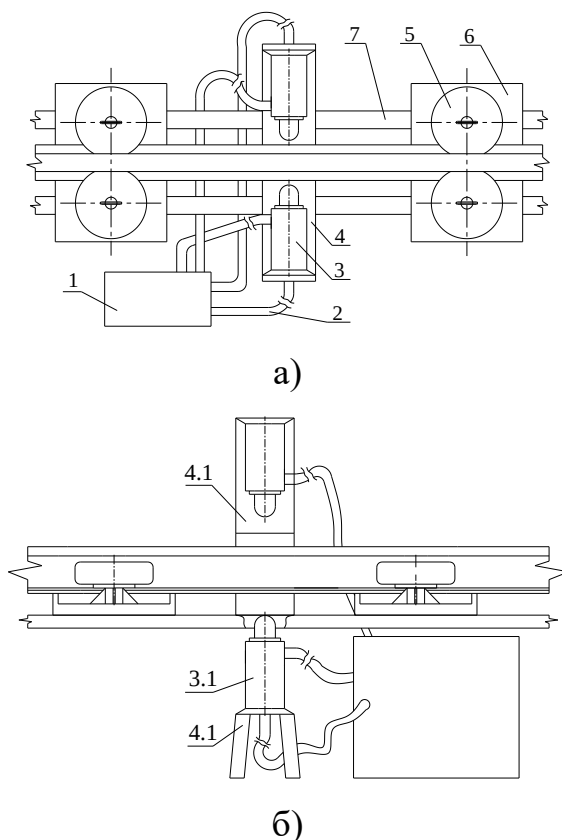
Принципиальная схема устройства правки сварного стыка (а, б)
